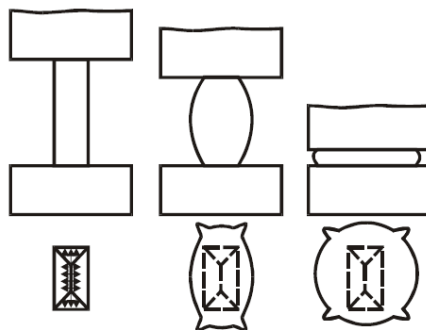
Схема движения частиц металла при осадке заготовки прямоугольного сечения
